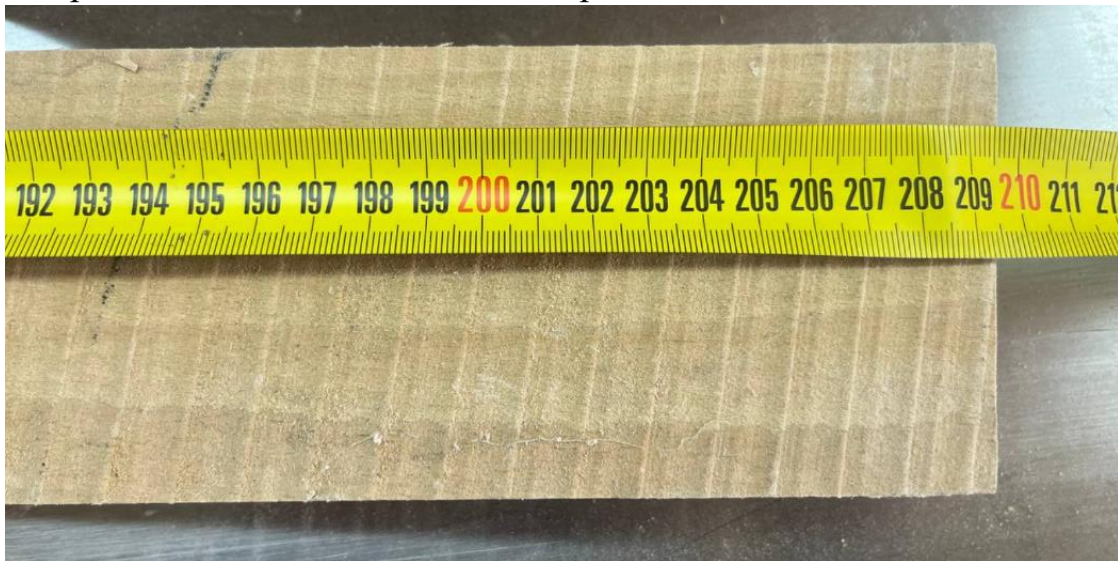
Приклад вимірювання довжини чорнової заготовки
